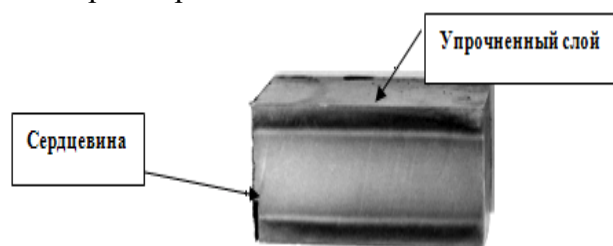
Схема расположения исследуемых поверхностей образца стали 60ПП
